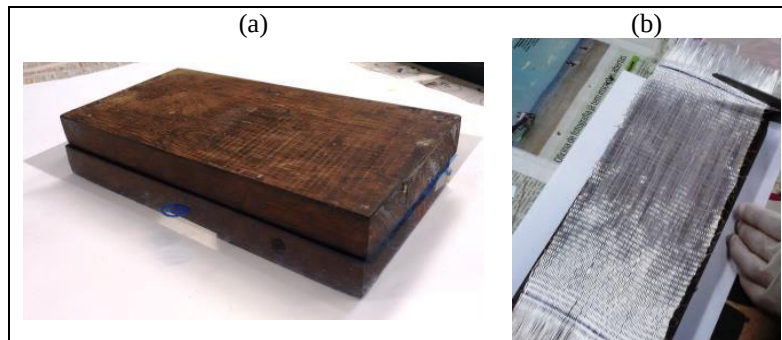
(a) Molde superior e inferior de madeira (b) Corte da lâmina de vidro nas dimensões do molde.
